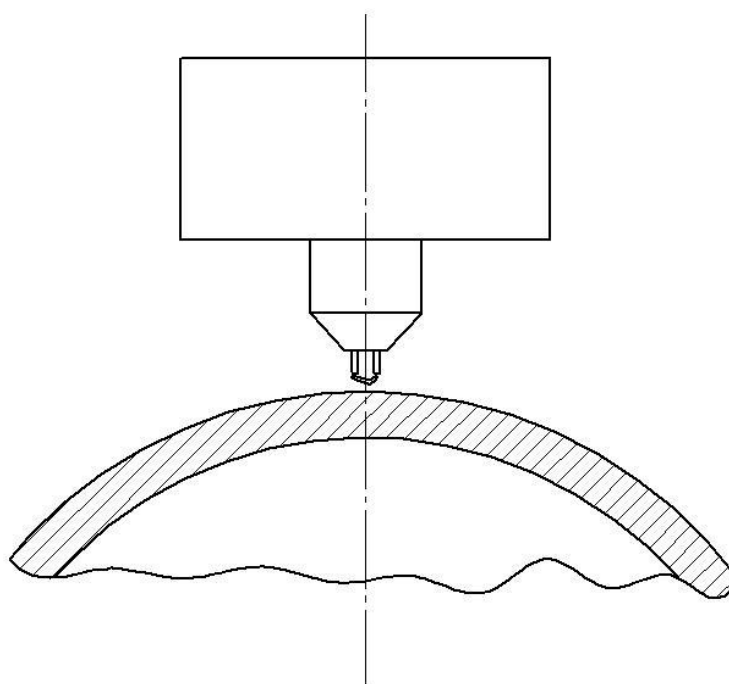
Схема сварки косвенной дугой
